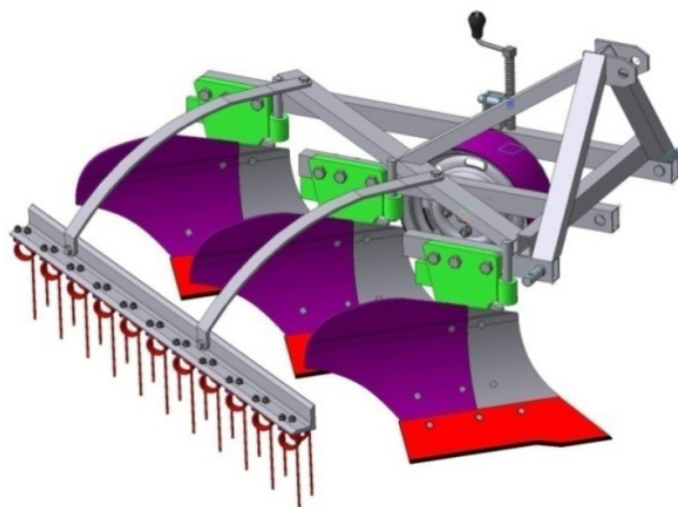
3D-модель малогабаритного пахотного агрегата ПЛН-3-35М с бороней-выравнивателем с пружинными зубьями
